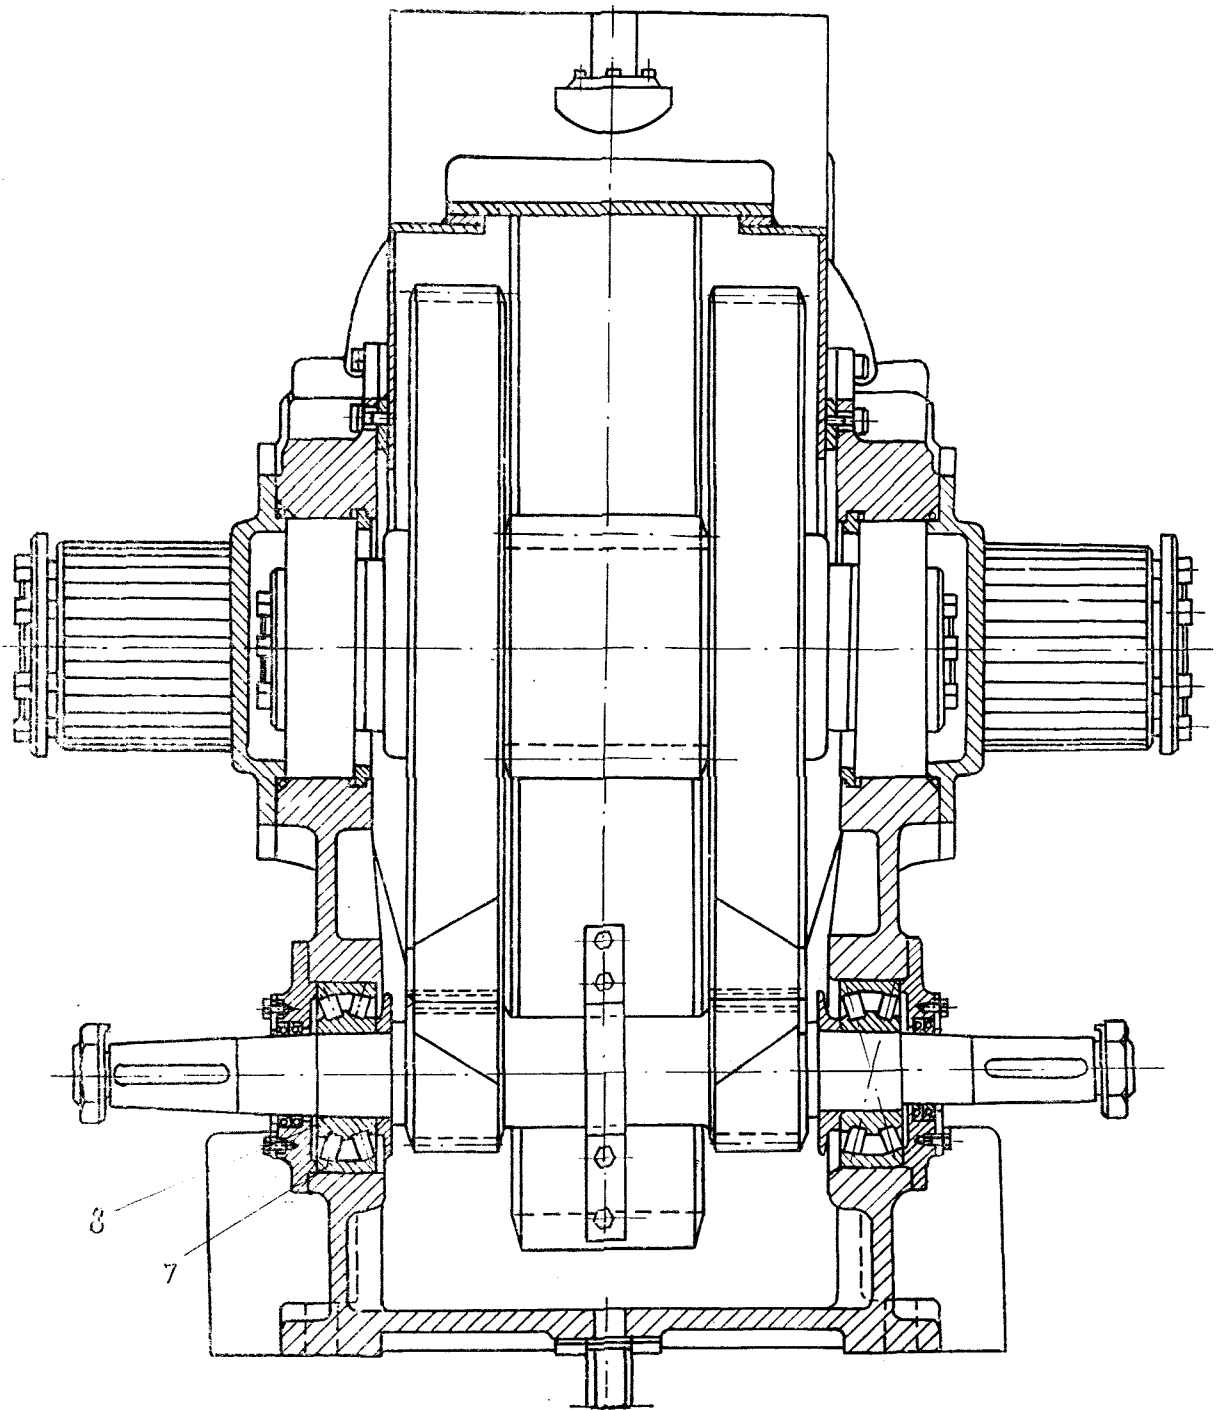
Редуктор подъемной лебедки (вид 2)
